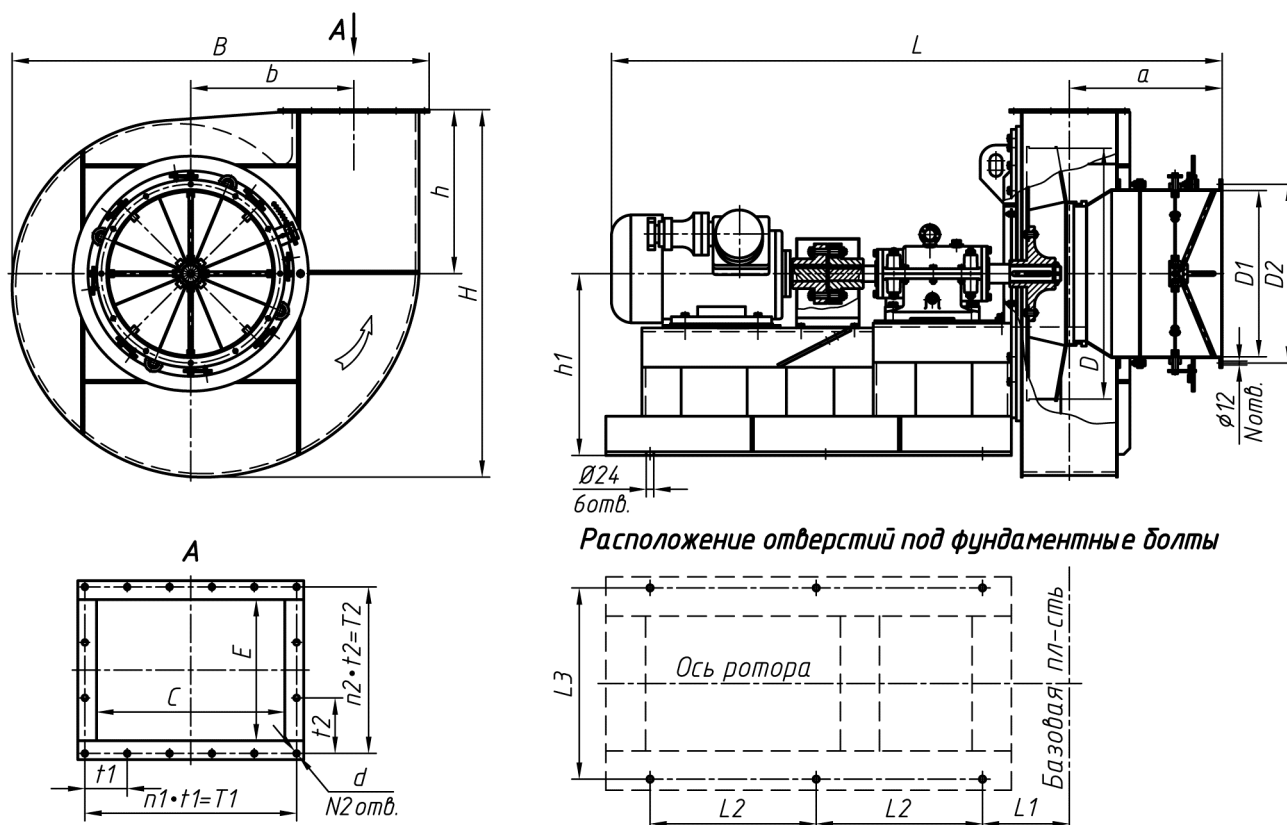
Габаритные и присоединительные размеры центробежных тягодутьевых машин исполнения 3 ВДН, ДН №6,3-13.
